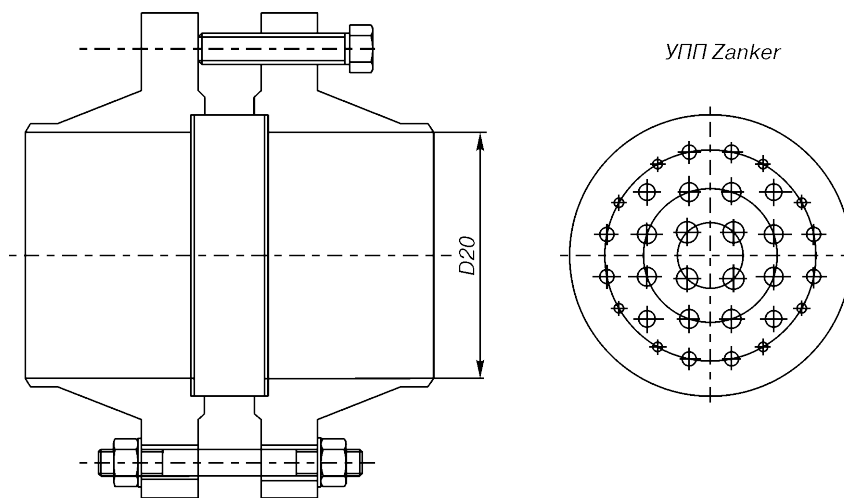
Схема дискового устройства подготовки потока Zanker.
